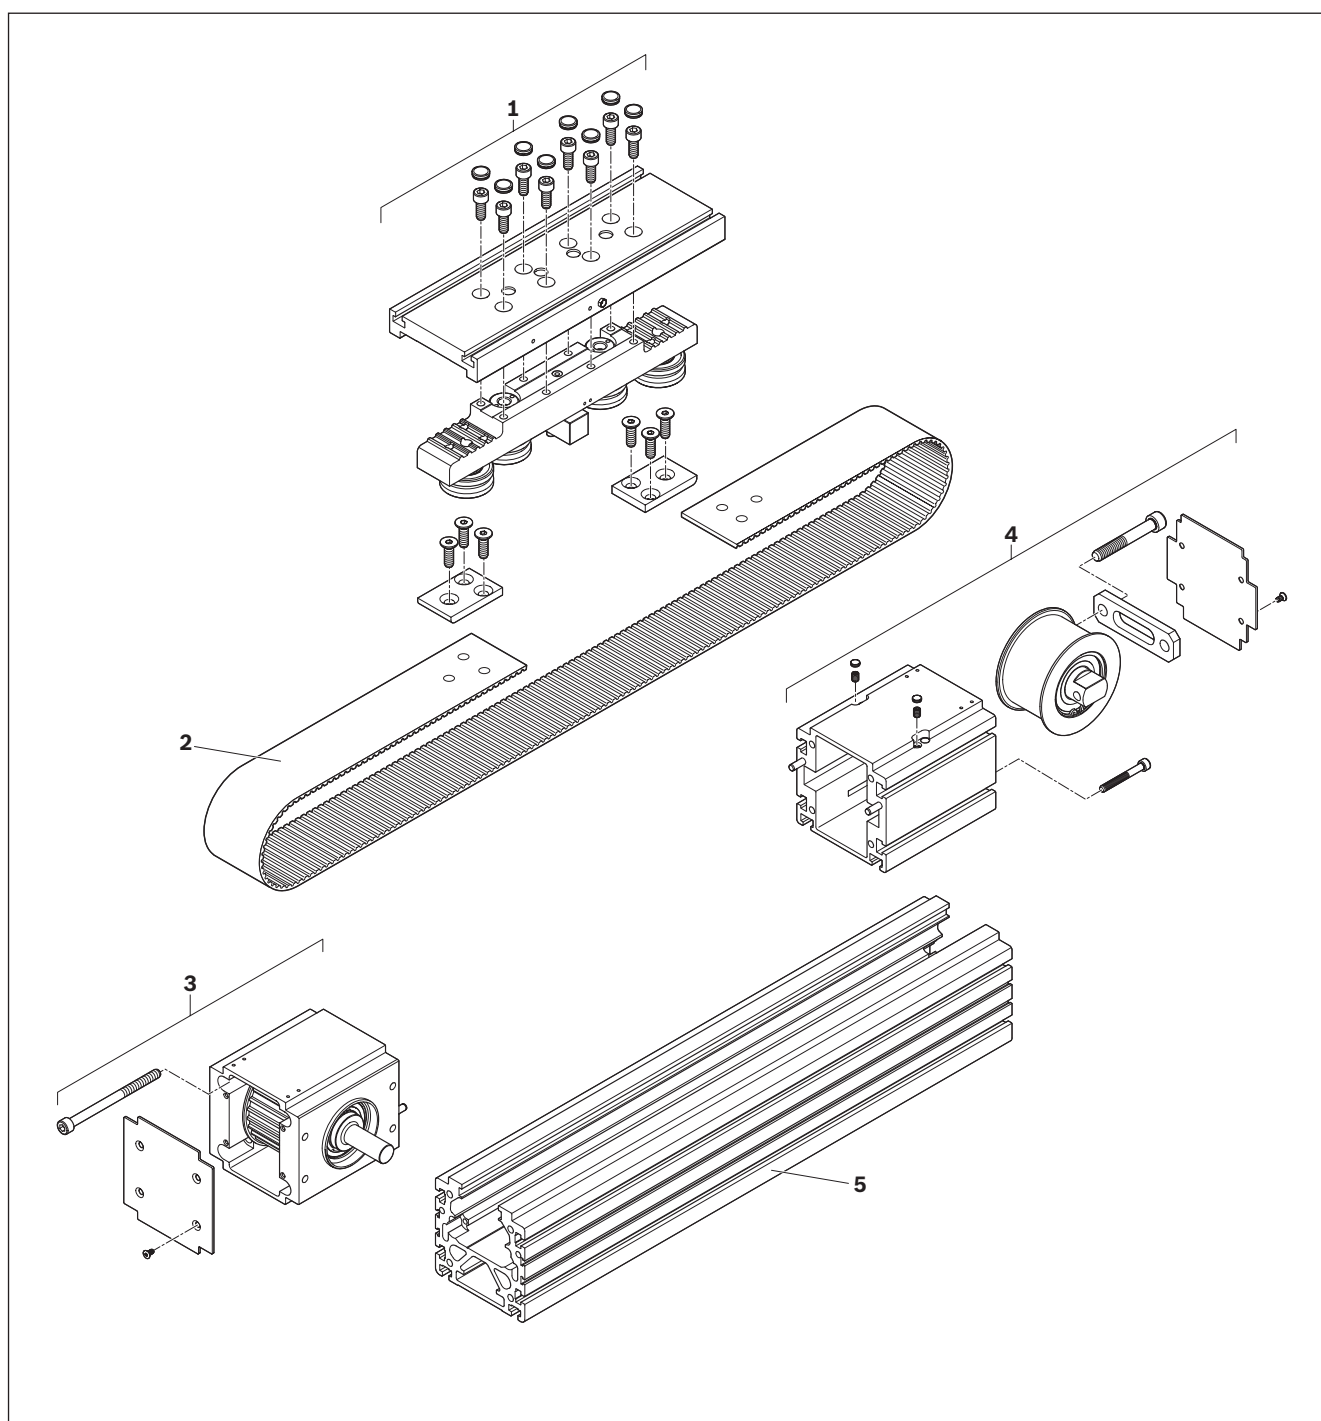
Vue d'ensemble MLR-080/-110-NN-3
